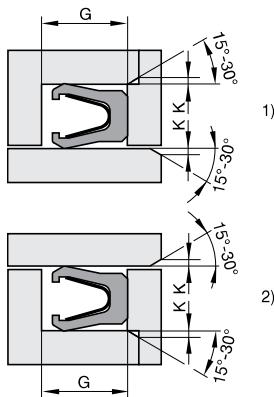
Установка составной посадочной канавки «губками вперед»;
